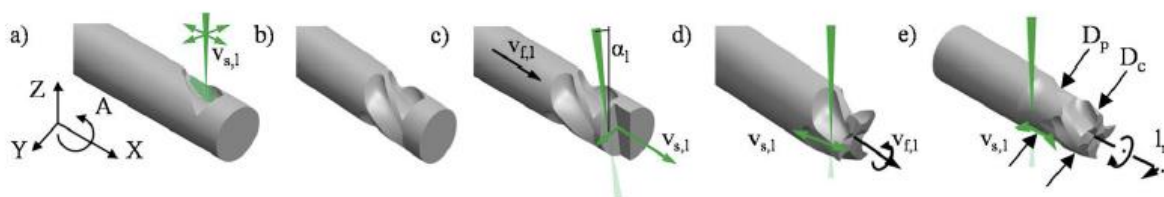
Úprava makrogeometrie řezné hrany laserovým obráběním - firma Hofmeister [51]
